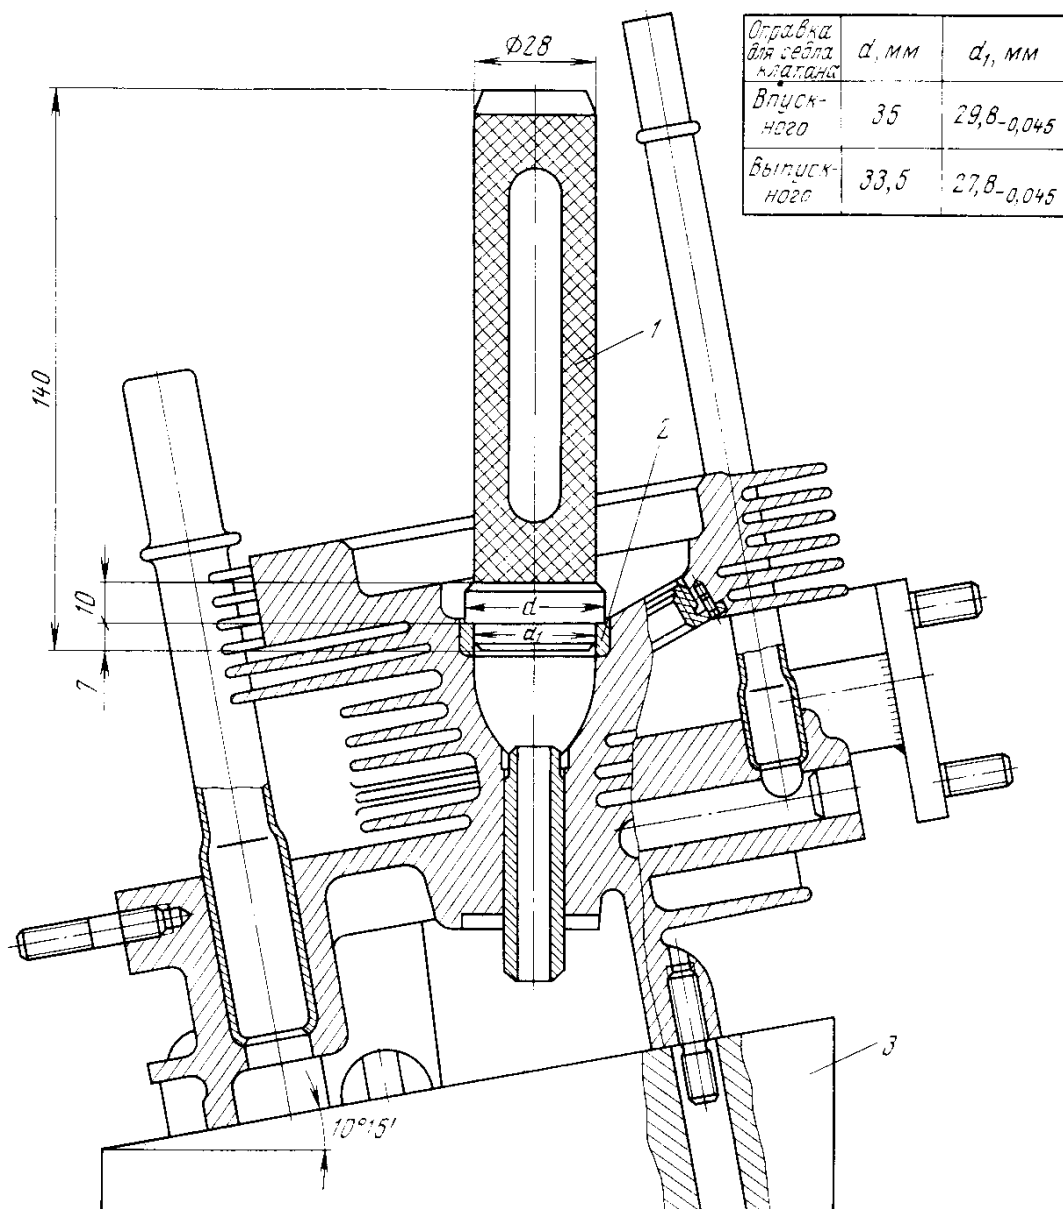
Оправка для запрессовки седла клапана: 1—оправка; 2—седло клапана; 3—подставка
